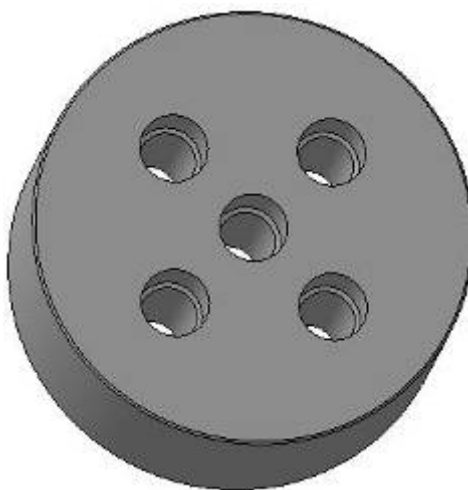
Модель для проведения исследований по запрессовке твердосплавных зубков
